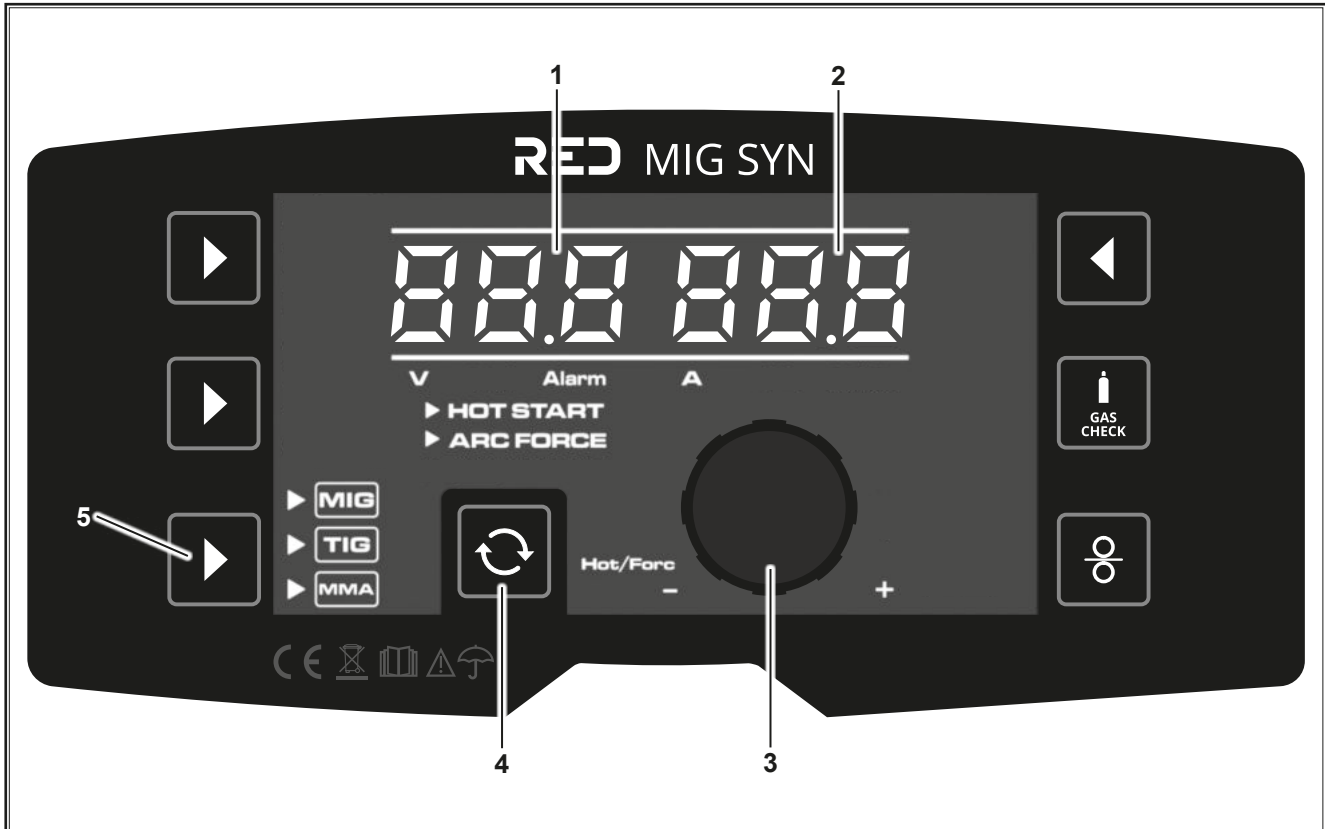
Indicación Proceso de soldadura Electrodo
